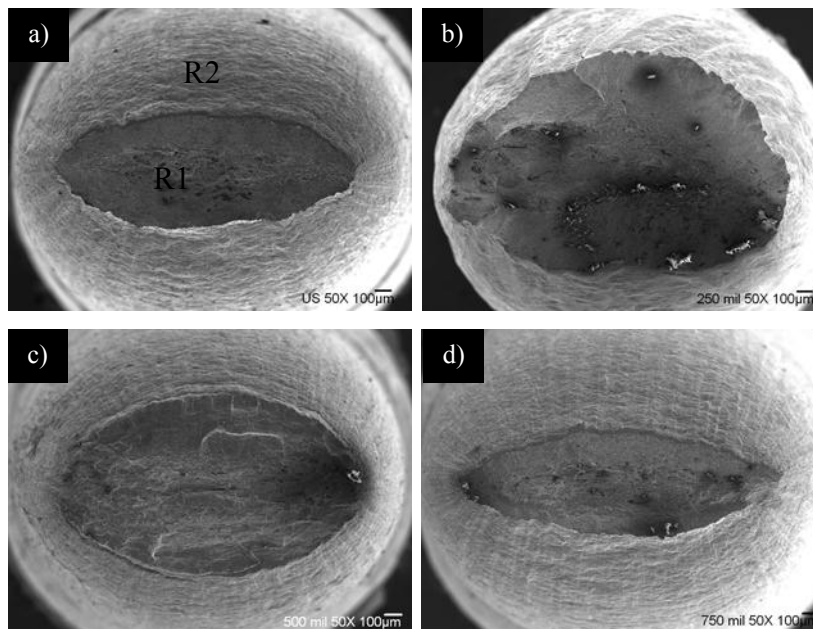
Modo de falla de a) ensayo de tensión de unión soldada, b) unión soldada con 25% de daño, c) unión soldada con 50% de daño y d) unión soldada con 75% de daño.
